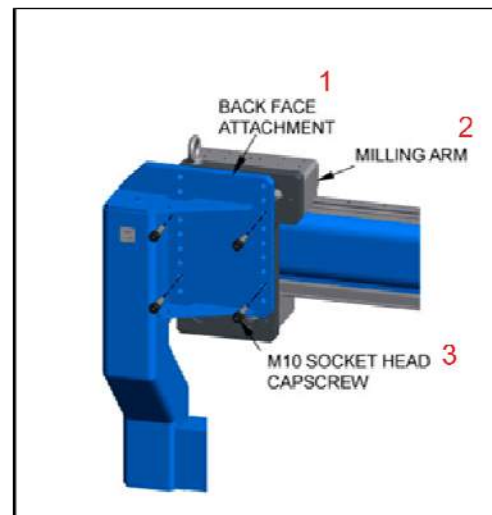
Детализовка узла насадки для обратной подрезки торца
